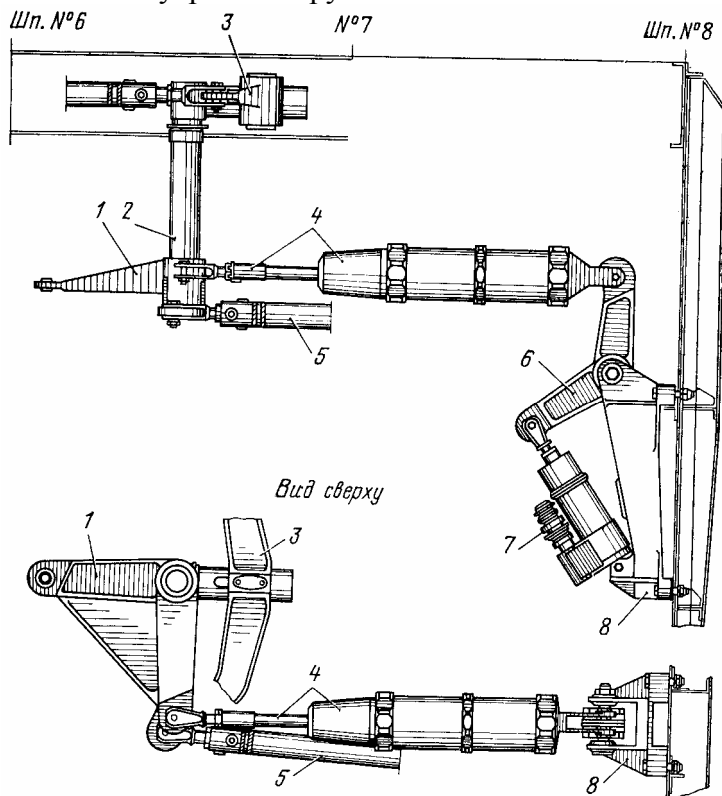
Установка взлетно-посадочного загрузителя руля направления:
